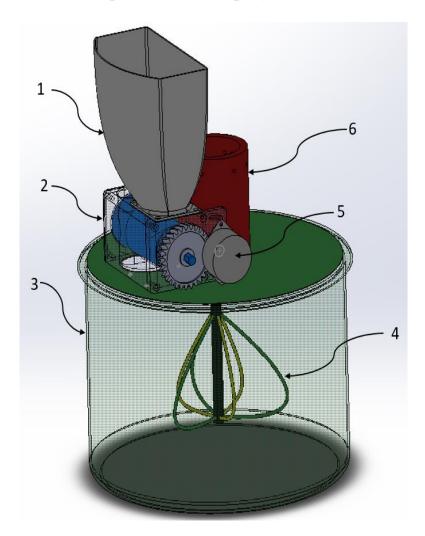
3D модель устройства. 1- емкость дозатора, 2- дозатор, 3- емкость для изготовления, 4-венчик, 5 – двигатель дозатора, 6 – держатель двигателя венчика
